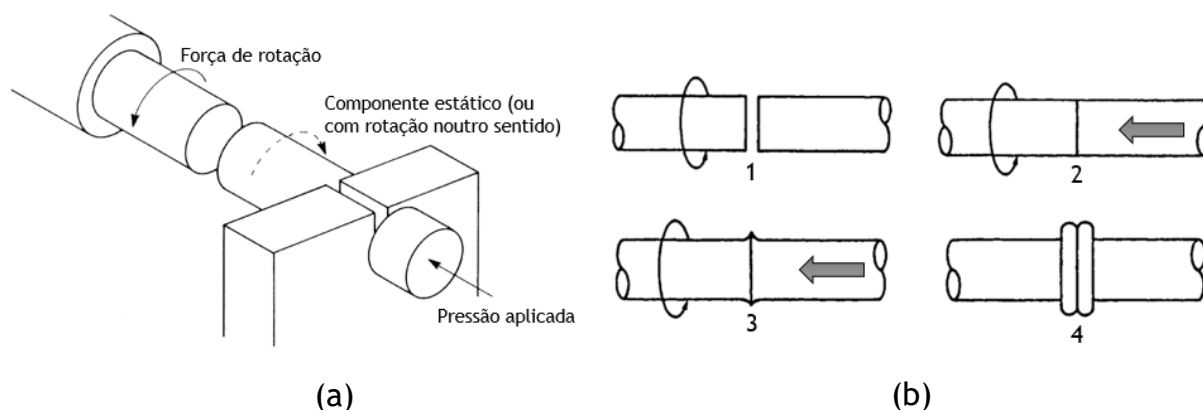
Processo de soldadura por fricção esquematizado: (a) posicionamento dos dois componentes a ligar; (b) 1- rotação de um componente; 2- Aplicação de pressão; 3- Deformação plástica; 4- União completa. Adaptado de [14].
